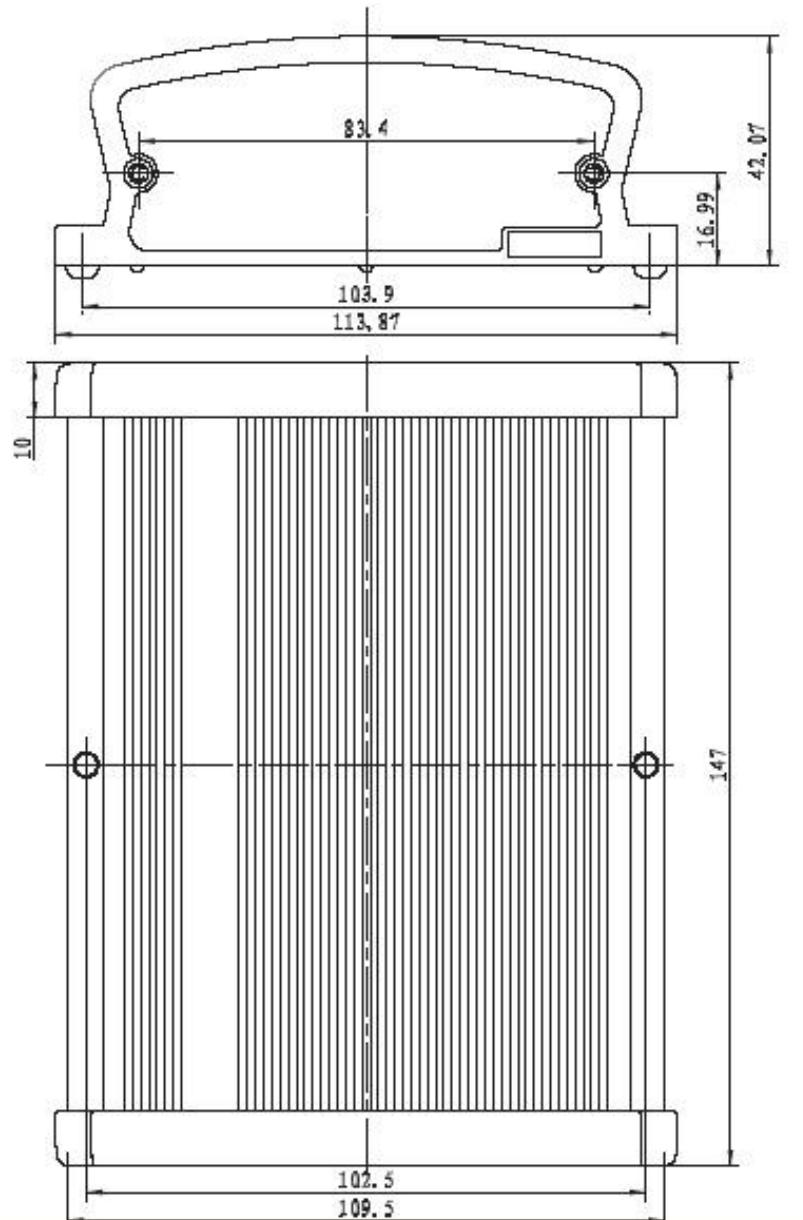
Габаритные размеры изделия ГАЛС-Т2М
